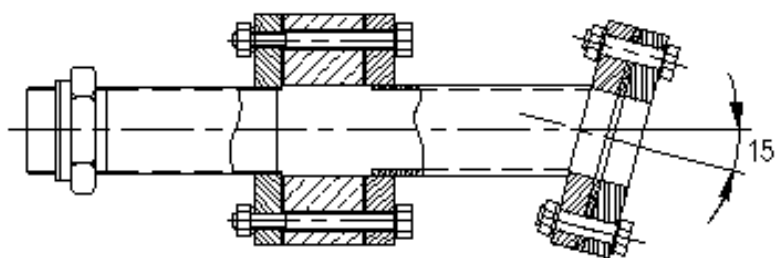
Схема установки маслоотводящего патрубка подшипника скольжения.
